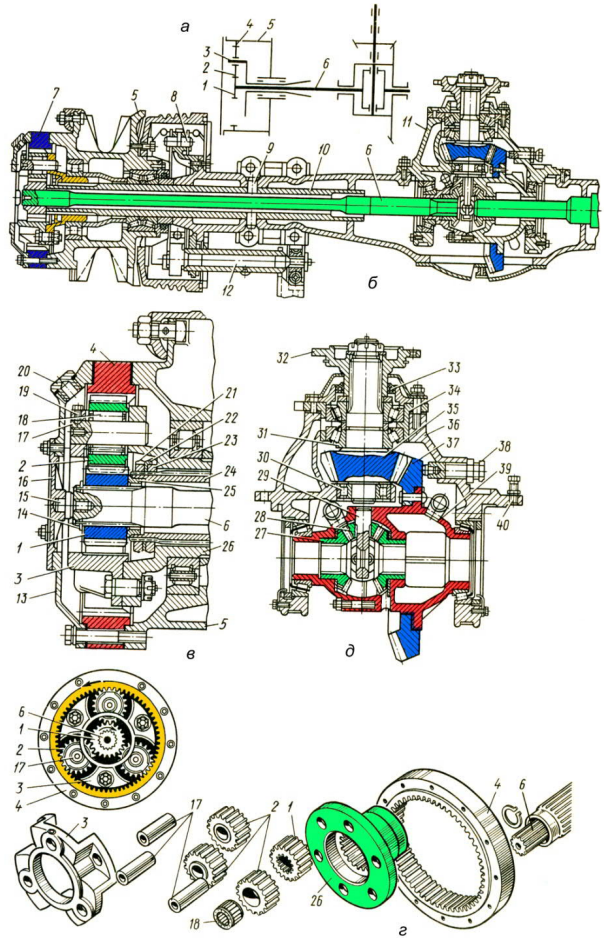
Задний мост грузового автомобиля МАЗ и его элементы:
